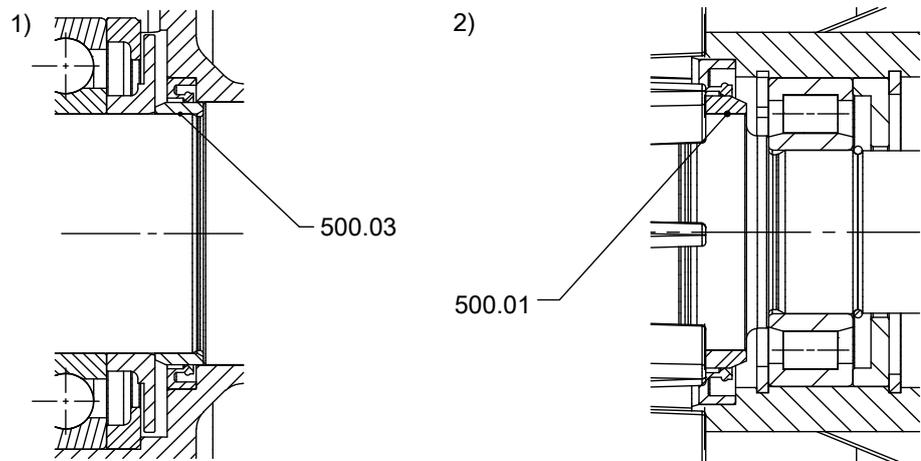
Cojinetes - Grupos motobomba sin sistema de refrigeración
